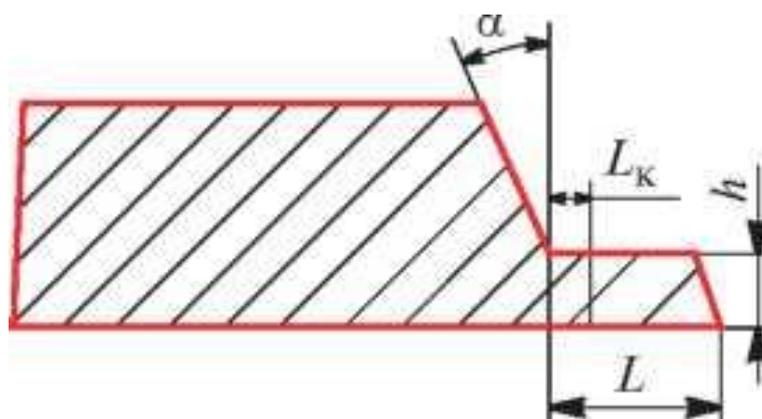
Разделка торцов труб под комбинированную сварку: h — толщина корневого шва; L — длина участка кромок корневого шва до сварки; L_k — длина корневого шва после сварки; α — угол наклона кромок [5]
